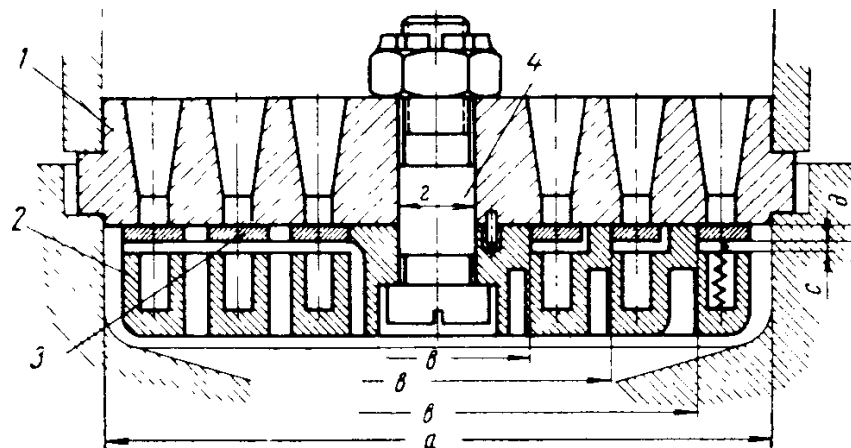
Клапан: 1 – сідло; 2 – упор; 3 – пластина; 4 – болт.
